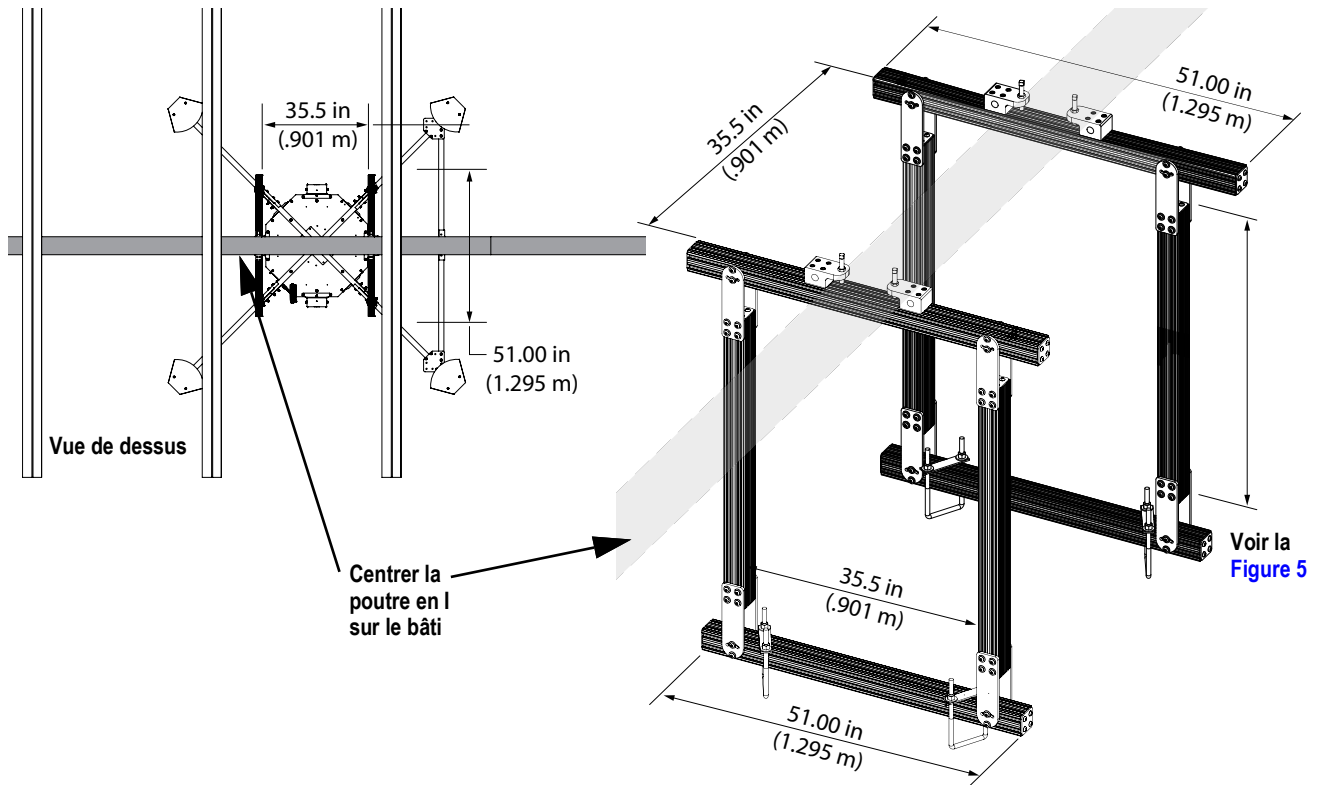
Calculs pour la longueur de coupe des barres 80/20 pour configuration sur ailes de poutre en I
